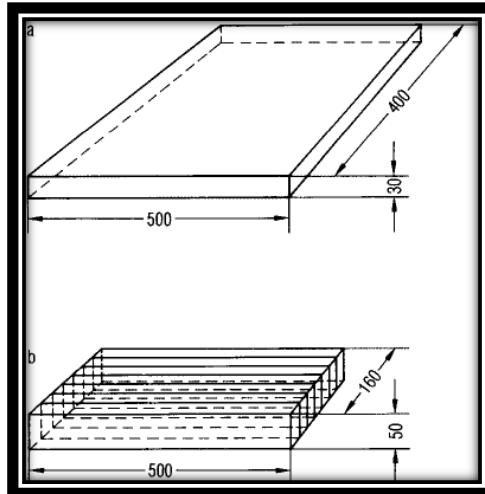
Tipos de bandeja de liofilização (adaptado de 27)
